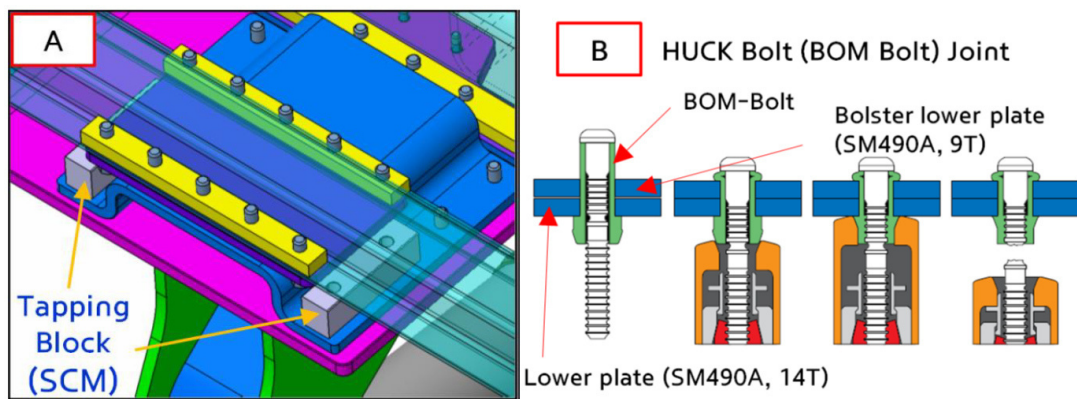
Вузол гасника коливань виляння, модернізація 2: а) вид зверху; б) болтові з'єднання (huck bolt).
